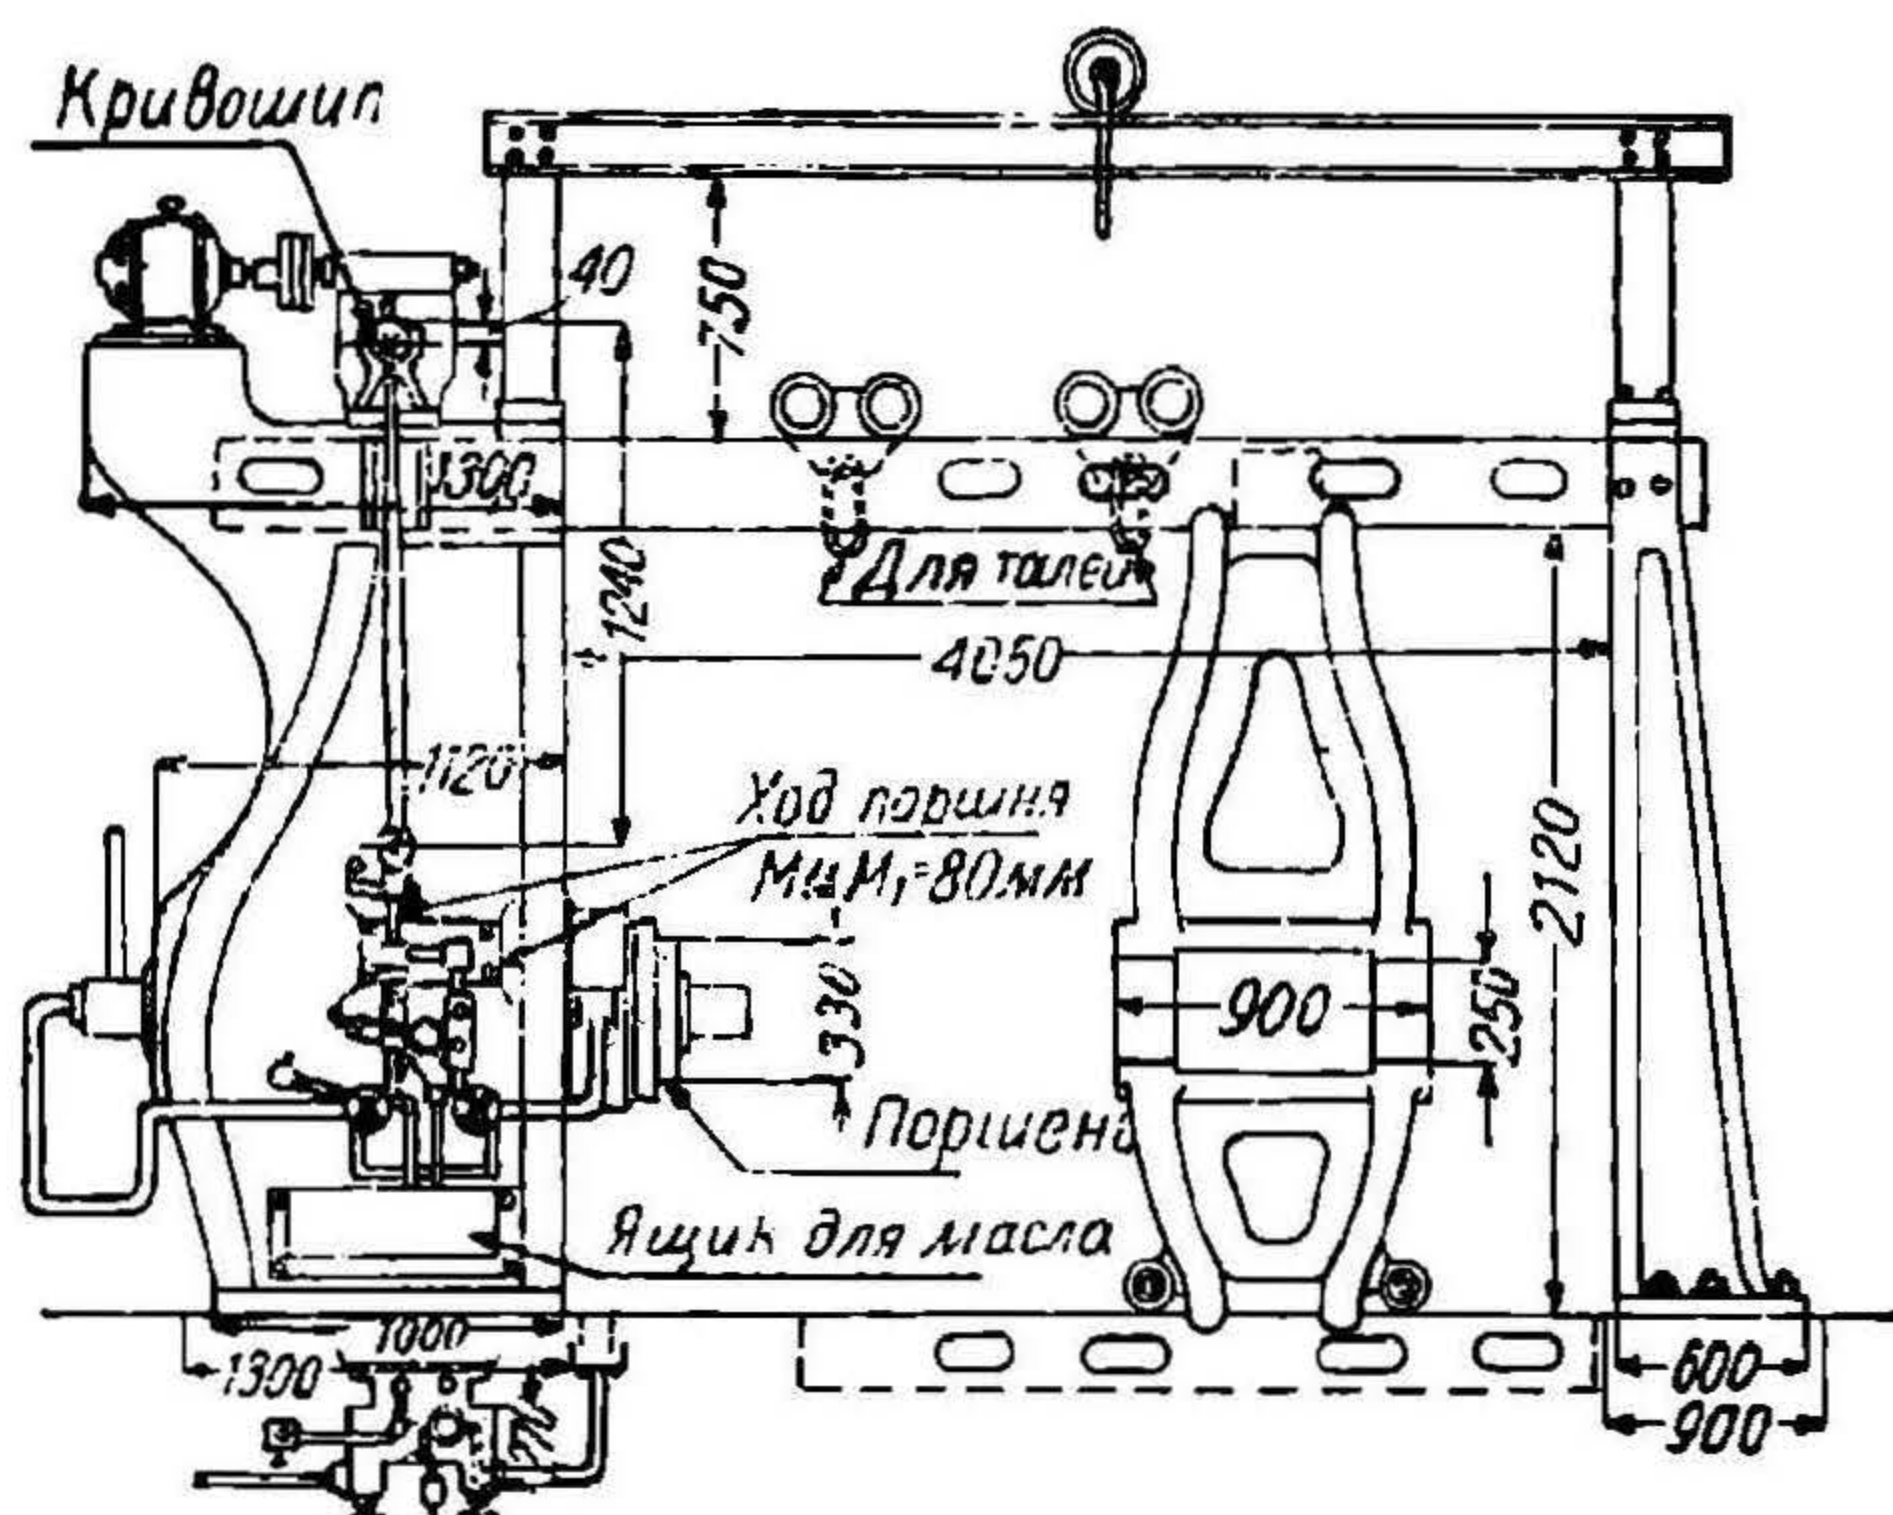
Универсальный гидравлический пресс для съёмки и насадки колес
